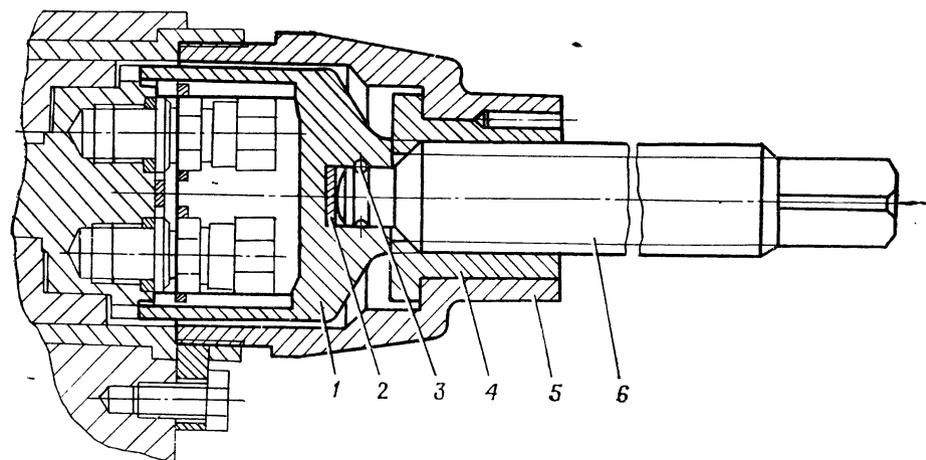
Установка приспособления 41.140 для оттягивания ствола:
